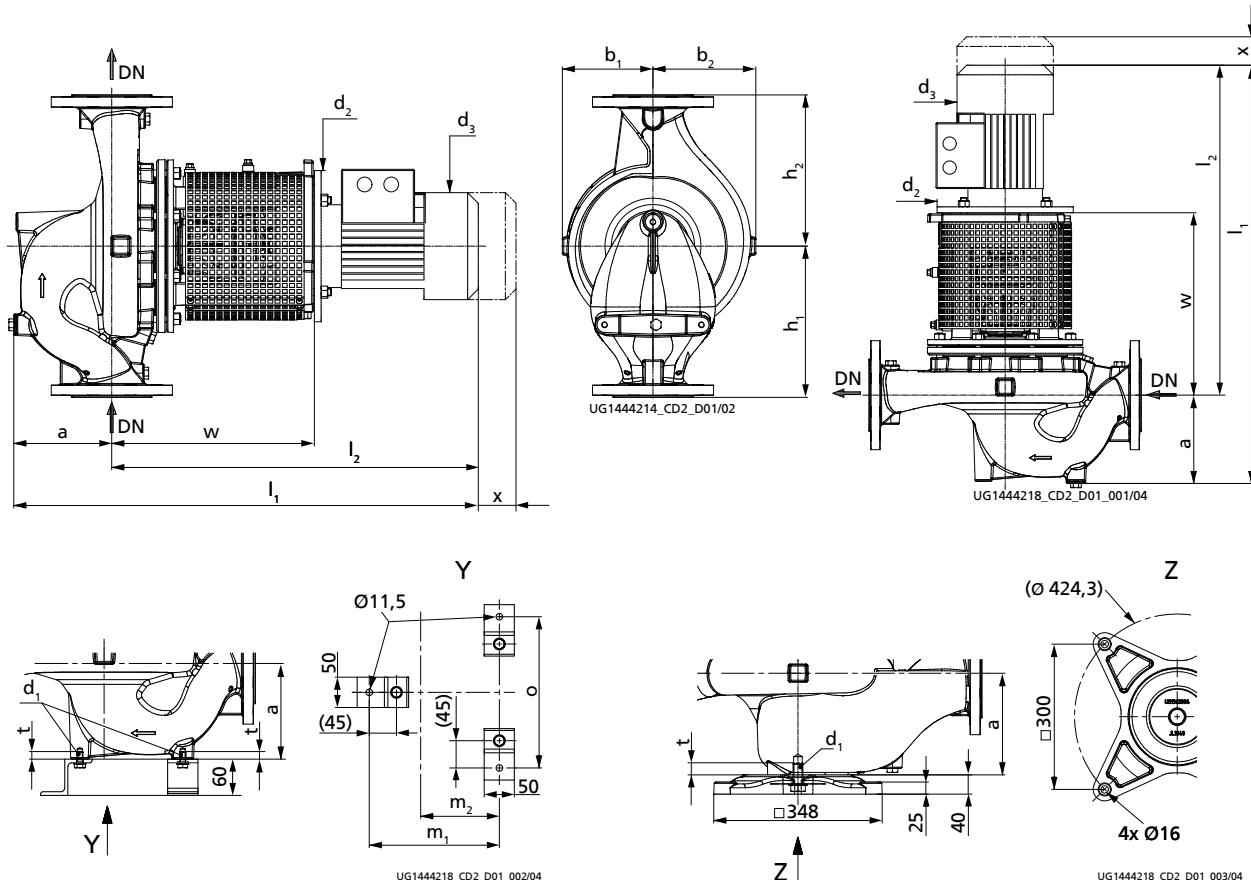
Dimensiones del grupo motobomba, dimensiones de la fijación de la base en montaje vertical
